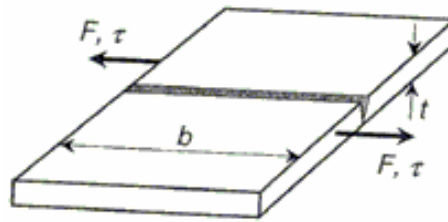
[8.15]. Стыковой сварной шов, подверженный сдвигу
